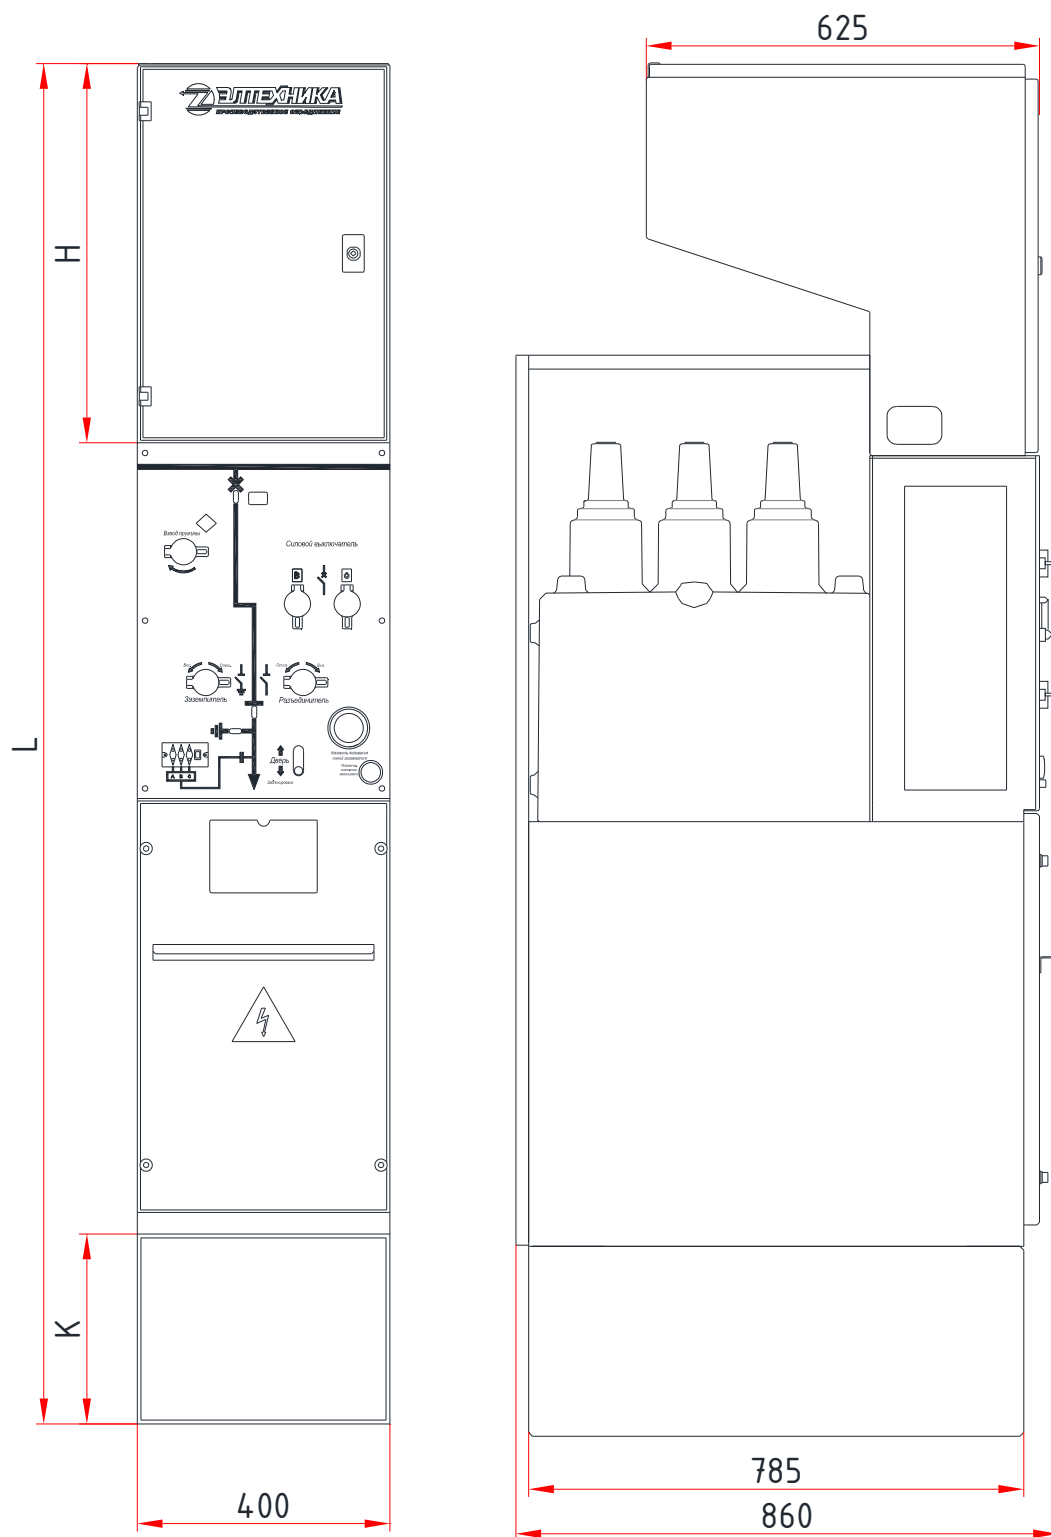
Габаритные размеры шкафов КРУ базовой конструкции на номинальный ток 630А.
